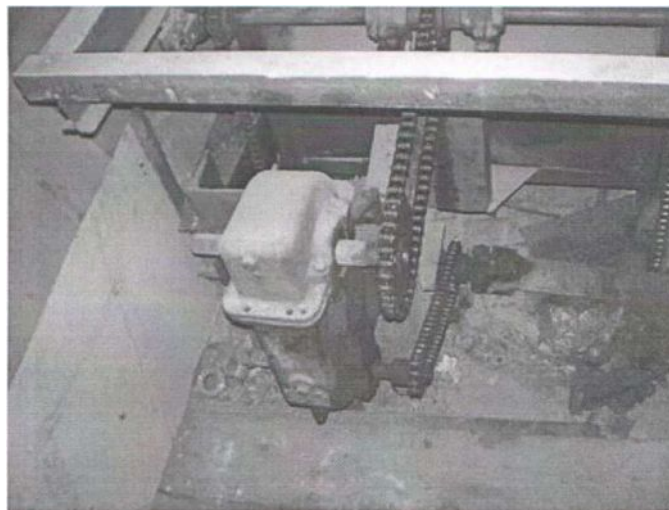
Передаточный механизм стенда с коробкой перемены передач и редуктором.
